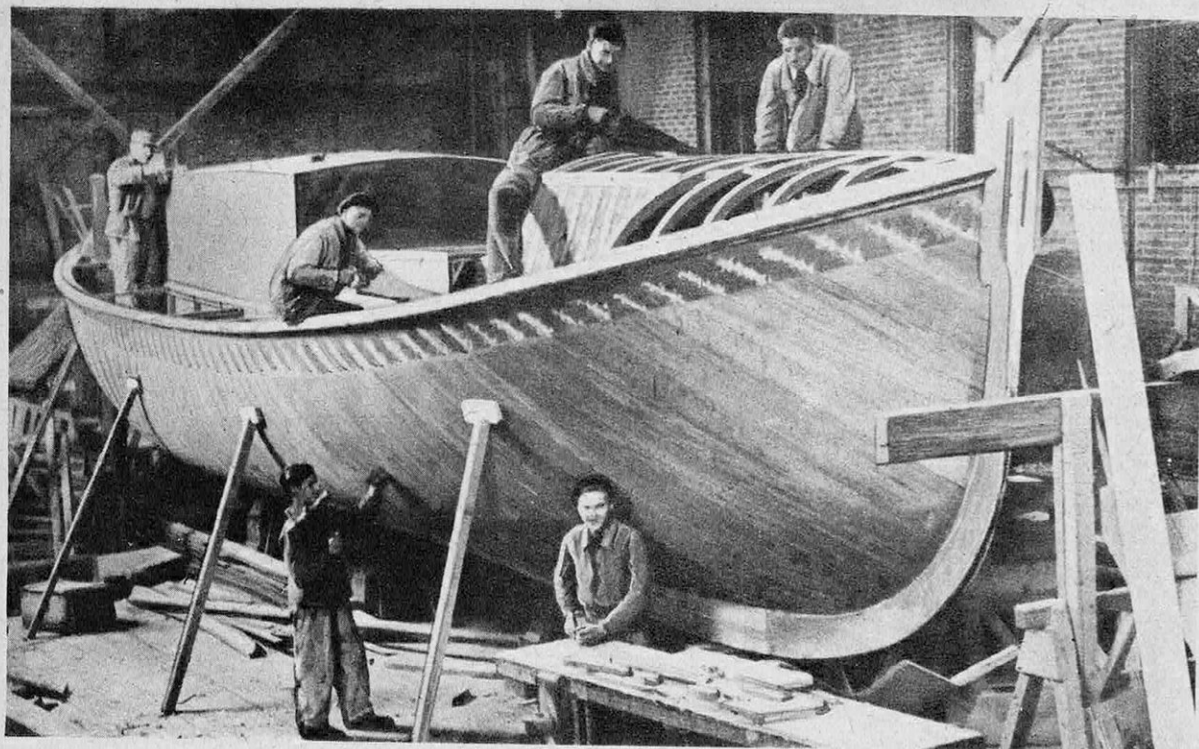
CANOT DE 13 M DESTINÉ A LA STATION DU CONQUET CONSTRUIT AU HAVRE (ATELIERS NORMAND)
